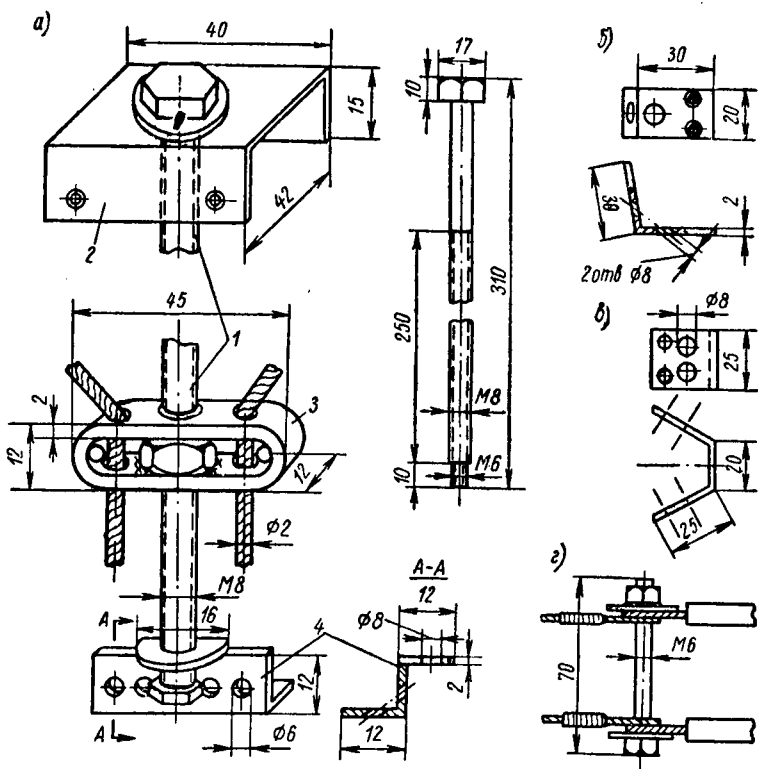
«Ладоба» МЗ-В. Элементы натяжного устройства: а — натяжное приспособление; б — верхняя направляющая скоба на углах транца; в — верхняя скоба в форштевне под трос и рым; г — болт крепления тросов и рыма.
